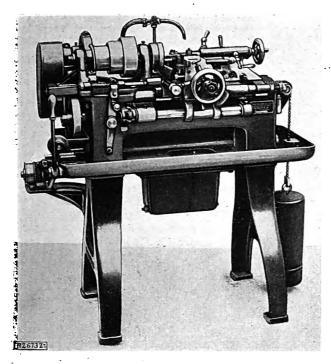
Halbselbsttätige Schneidbank für sehr genaue Schnecken und Gewinde
